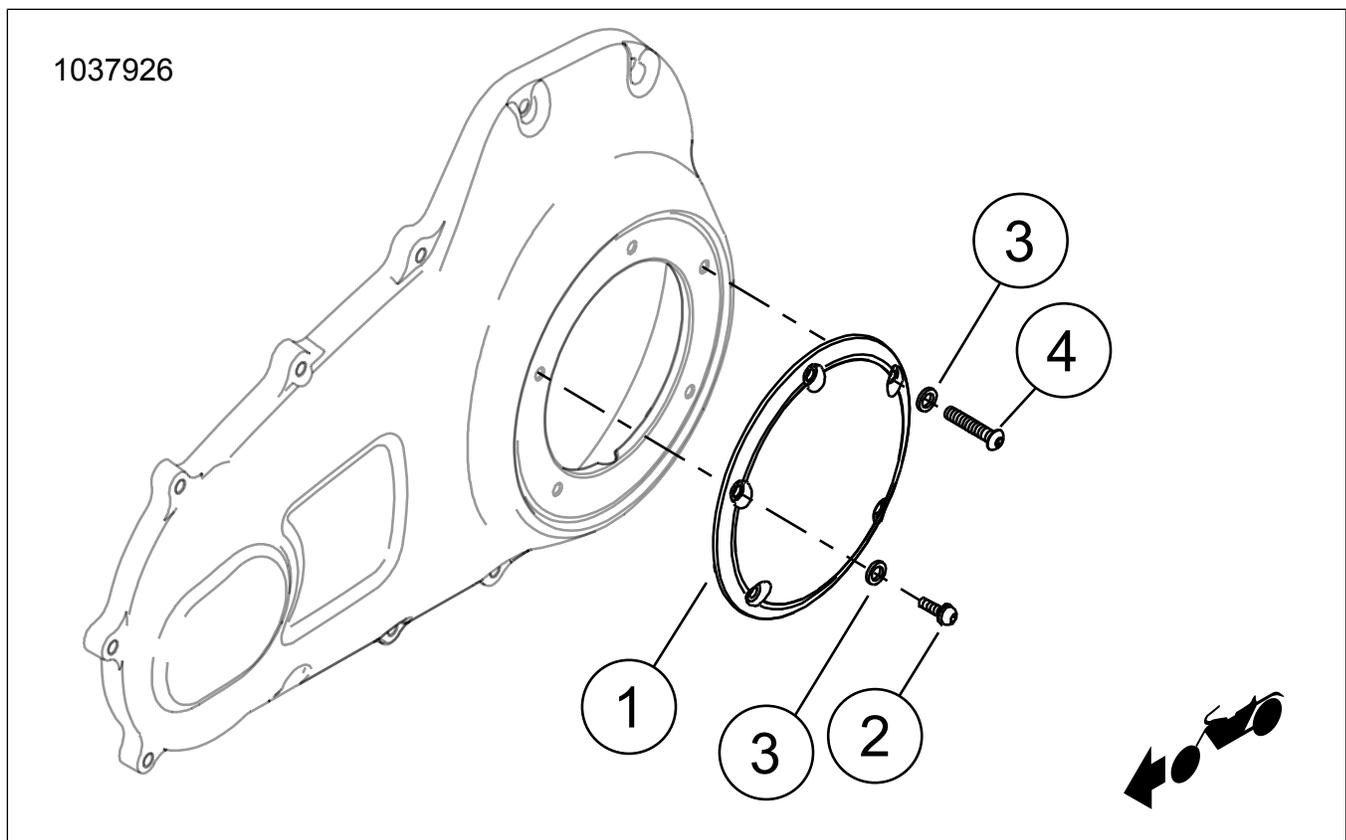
Conteúdo do kit: Componentes da tampa de inspeção da embreagem
